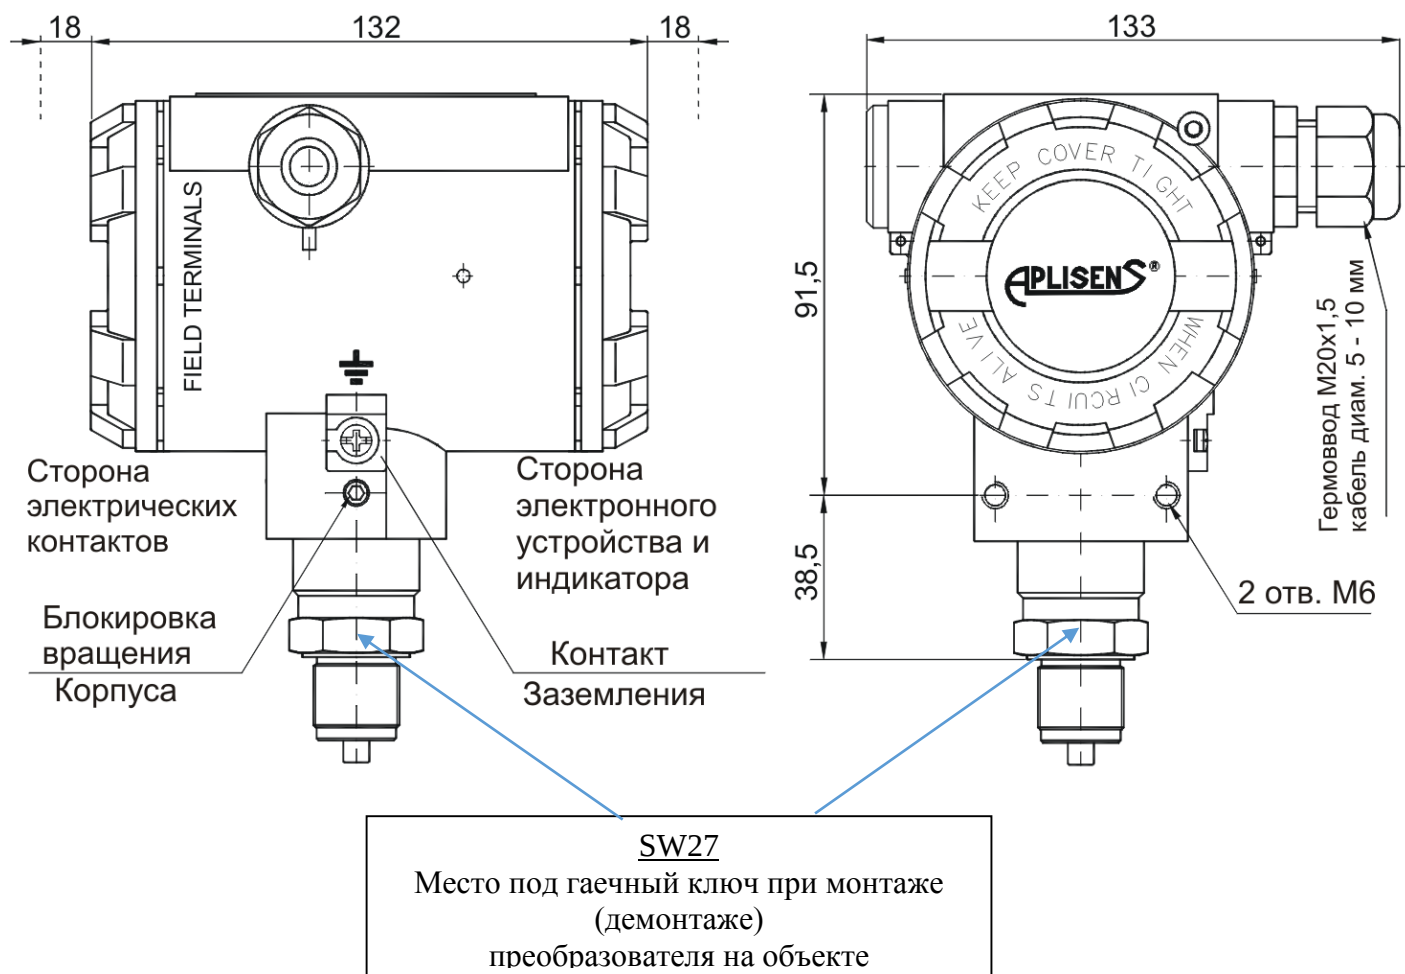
Внешний вид, установочные и присоединительные размеры преобразователей APC-2000.Safety/ALW
